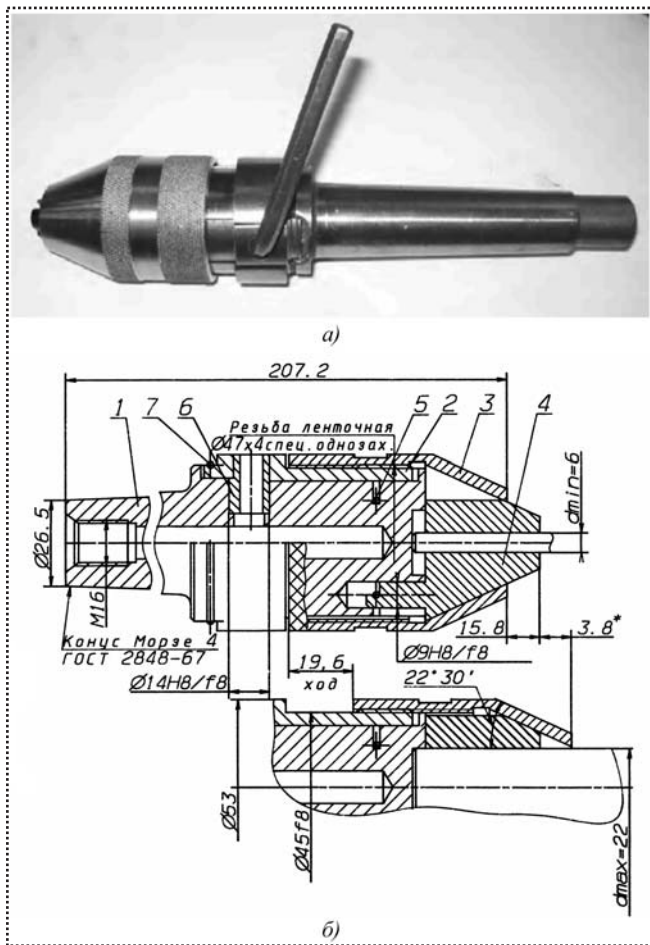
Широкодиапазонный эксцентриковый сверильно-фрезерный патрон с ключом типа ЭФПК-22:
